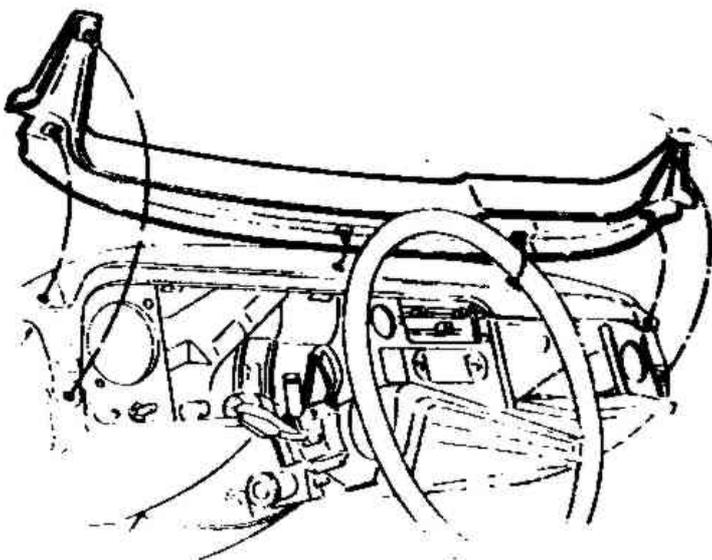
Точки крепления обивки приборного щитка (Разд.27)
